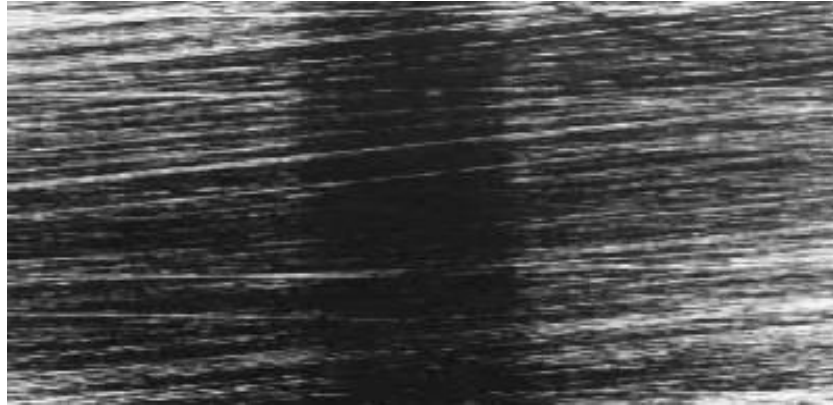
Corrosion de contact sur la bague Intérieure d'un roulement à rouleaux Sphérique [BEN22].
